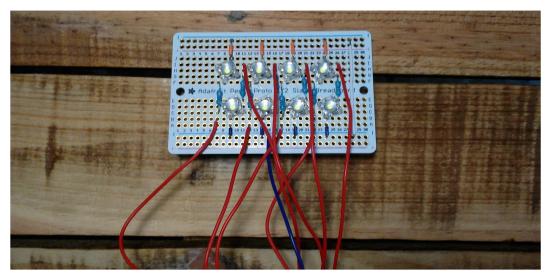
Placa de leds soldada, 2020, Noelia Medina.
